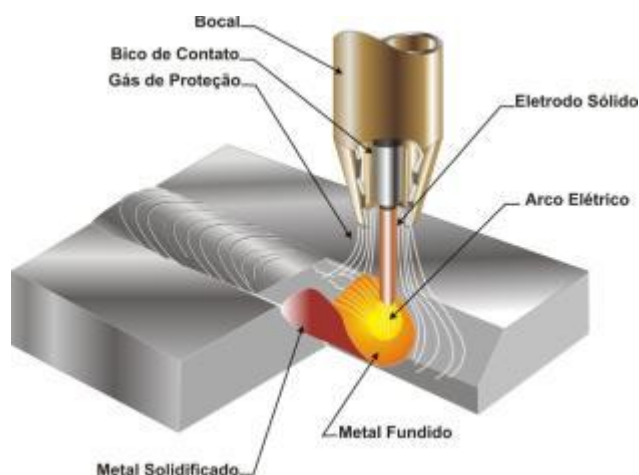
Detalhes de uma tocha de soldagem MIG/MAG [15]
